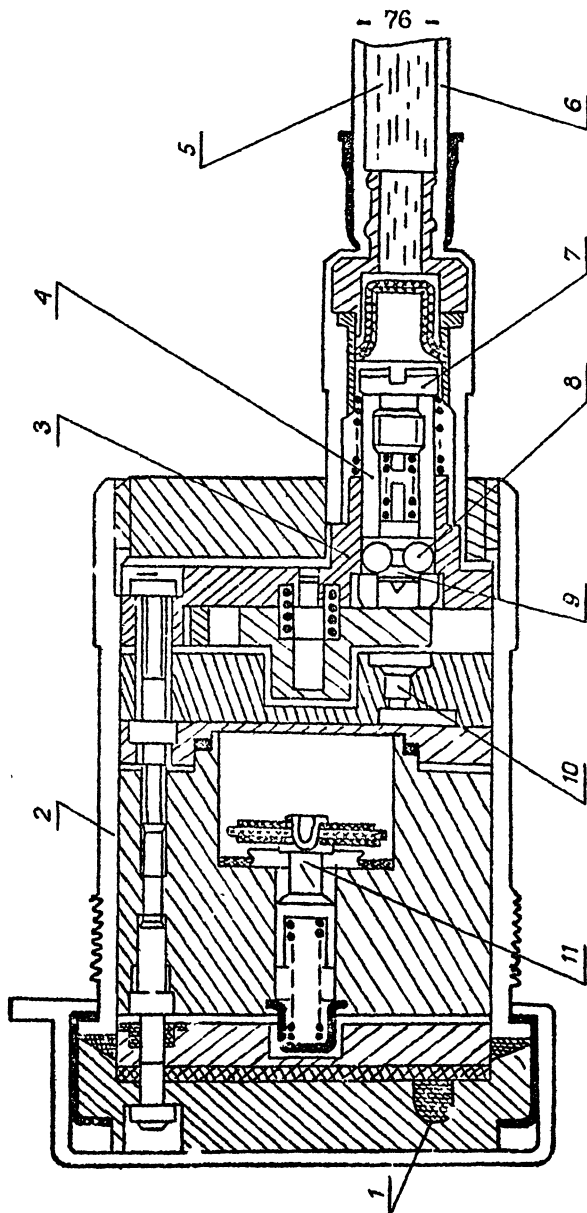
Расположение датчика цели в корпусе взрывателя МВД(Г):
